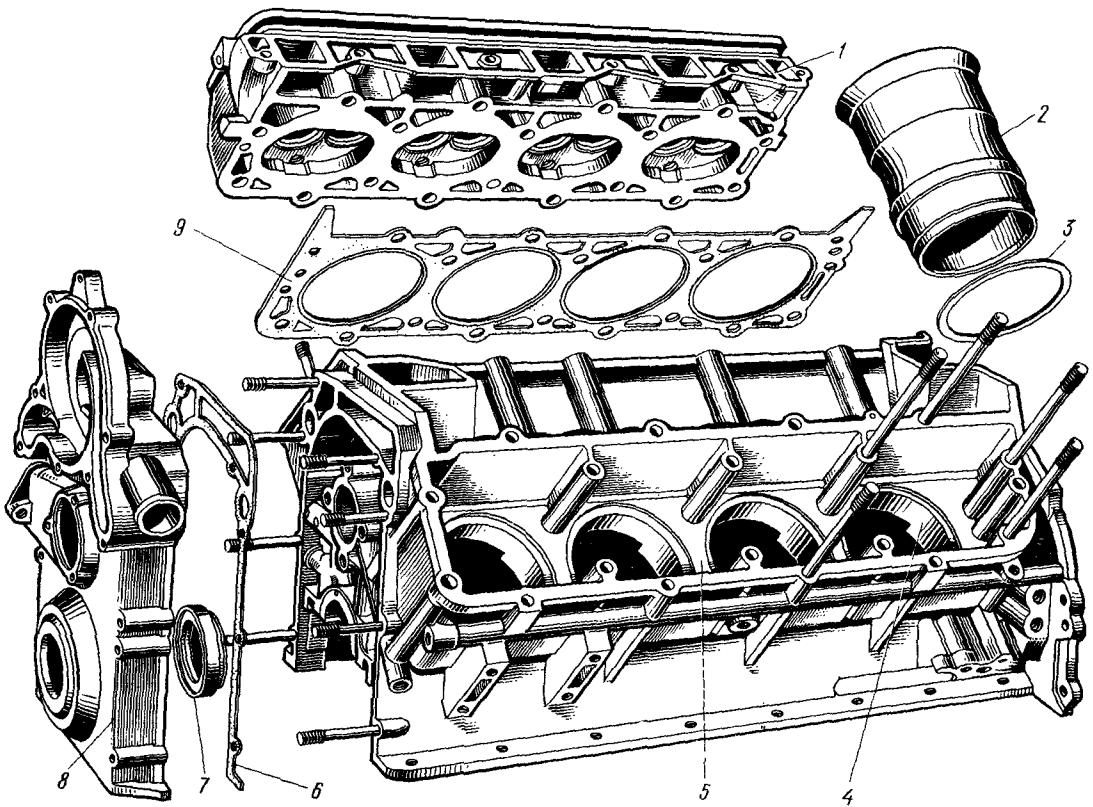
Головка и блок цилиндров V-образного восьмицилиндрового двигателя ЗМЗ-53:
